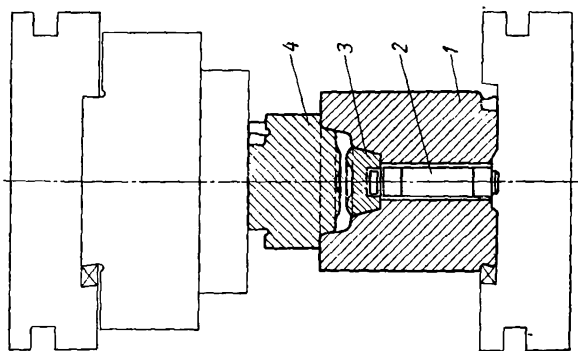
Штамп с верхним штампом-разгонкой для штамповки дисков: 1 — нижний штамп; 2 — стержень выталкивателя; 3 — выталкиватель; 4 — разгонка
